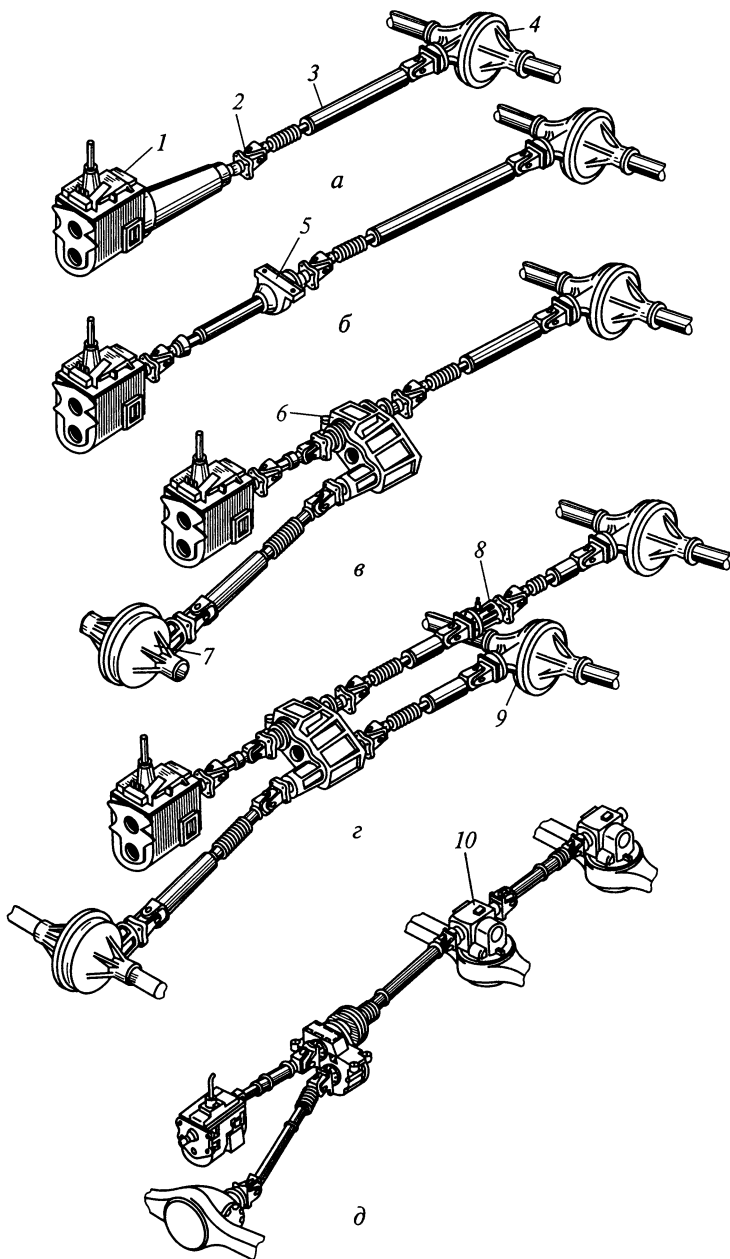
Карданные передачи для автомобилей с различными колесными формулами:
